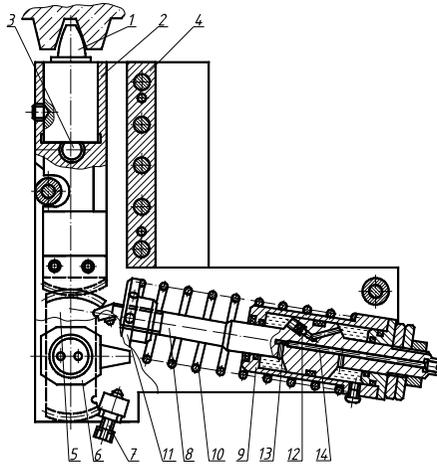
Устройство для обкатывания роликами клиноременных шкивов
